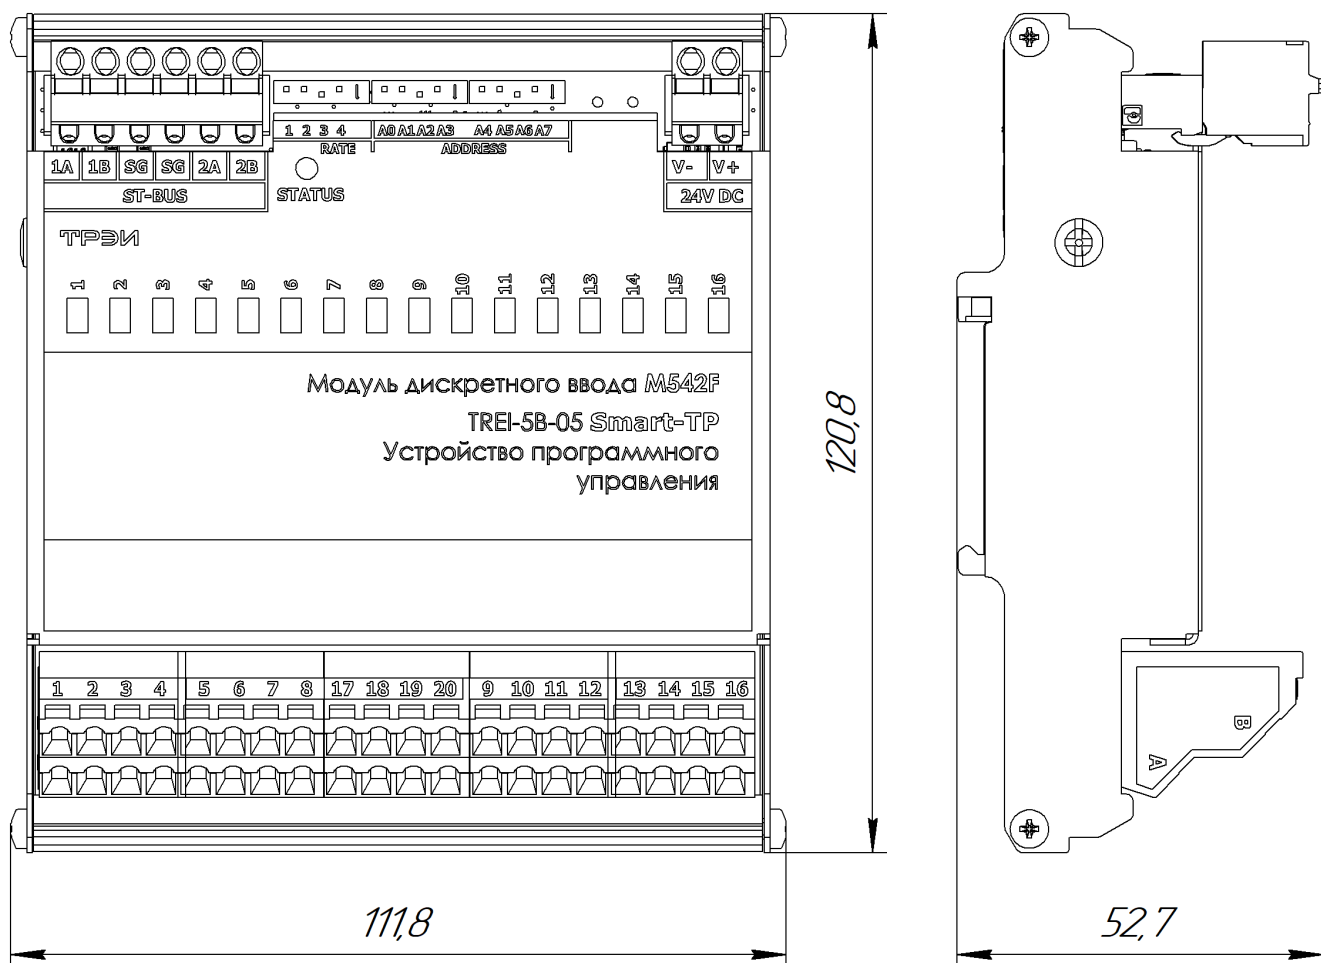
Чертеж общего вида M542F с указанием габаритных и присоединительных размеров
